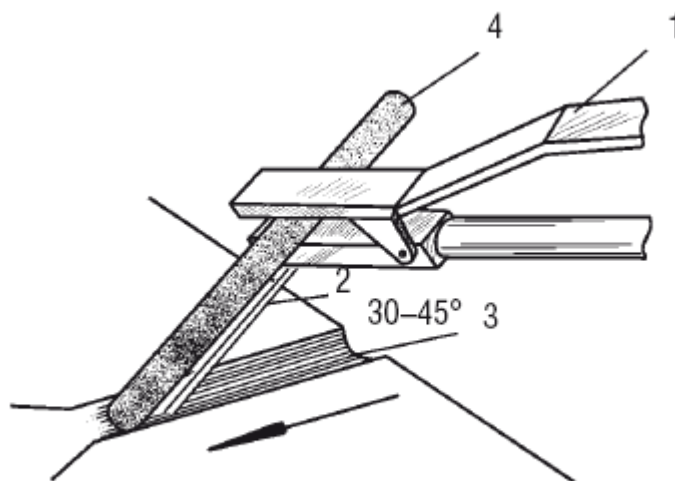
Схема осуществления воздушно-дуговой резки: 1 – резак; 2 – струя воздуха; 3 – канавка; 4 – электрод
